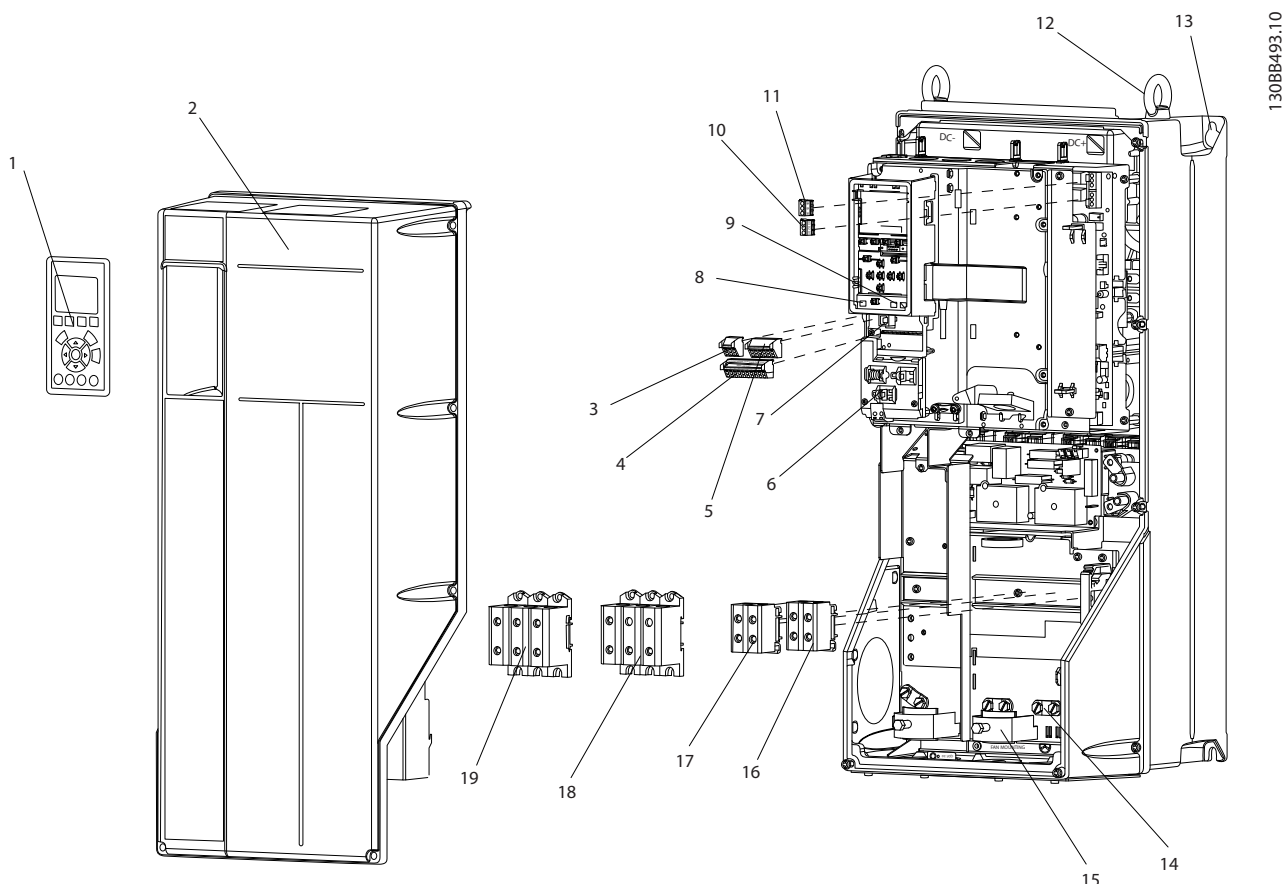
Explosionszeichnung A1-A3, IP20
